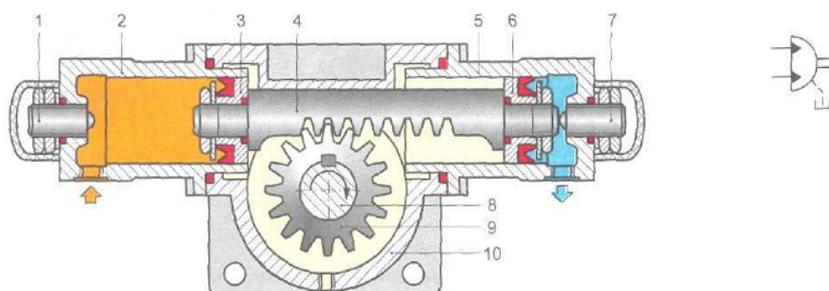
Поворотный гидродвигатель поршневого типа. 1,7 регулировочные винты; 2,5 – гильзы; 3,6 – поршни; 4 рейка; 8 – выходной вал; 9 – шестерня; 10 – корпус.
